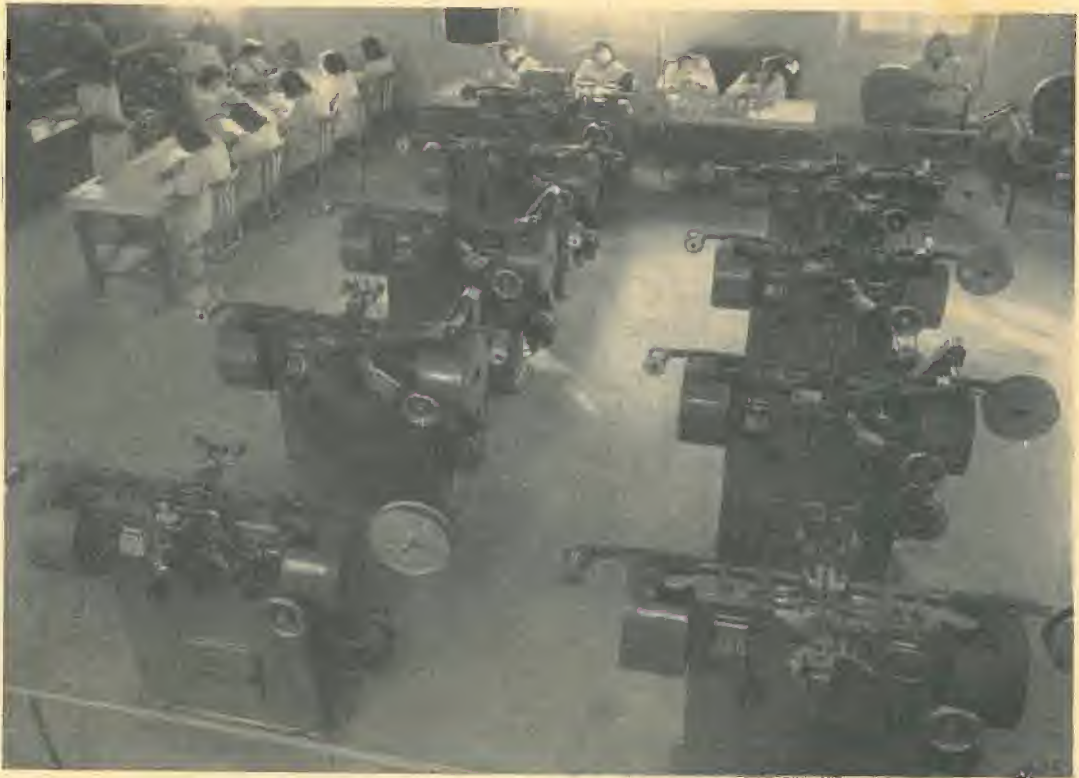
Macchine automatiche per la produzione degli « elettrodi ».
